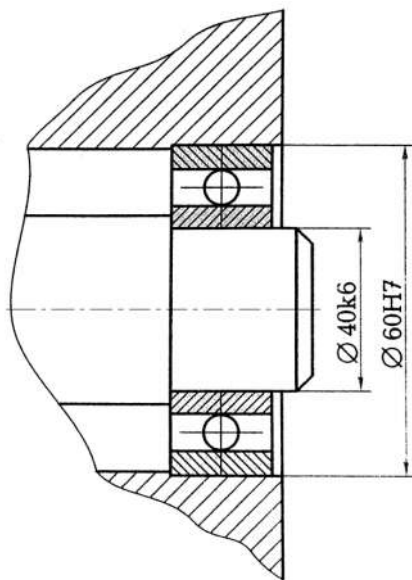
Пример обозначения на сборочном чертеже посадок подшипника качения
